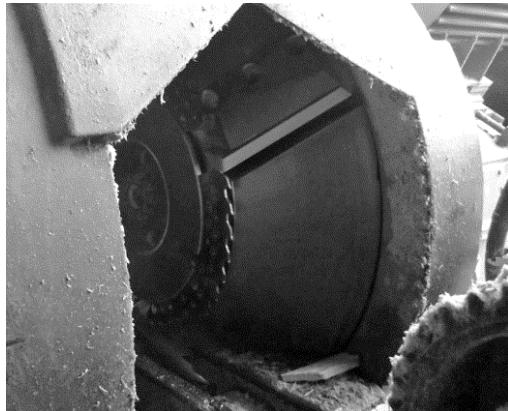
Малоножевая торцово-коническая фреза фрезерно-брюсующего станка
